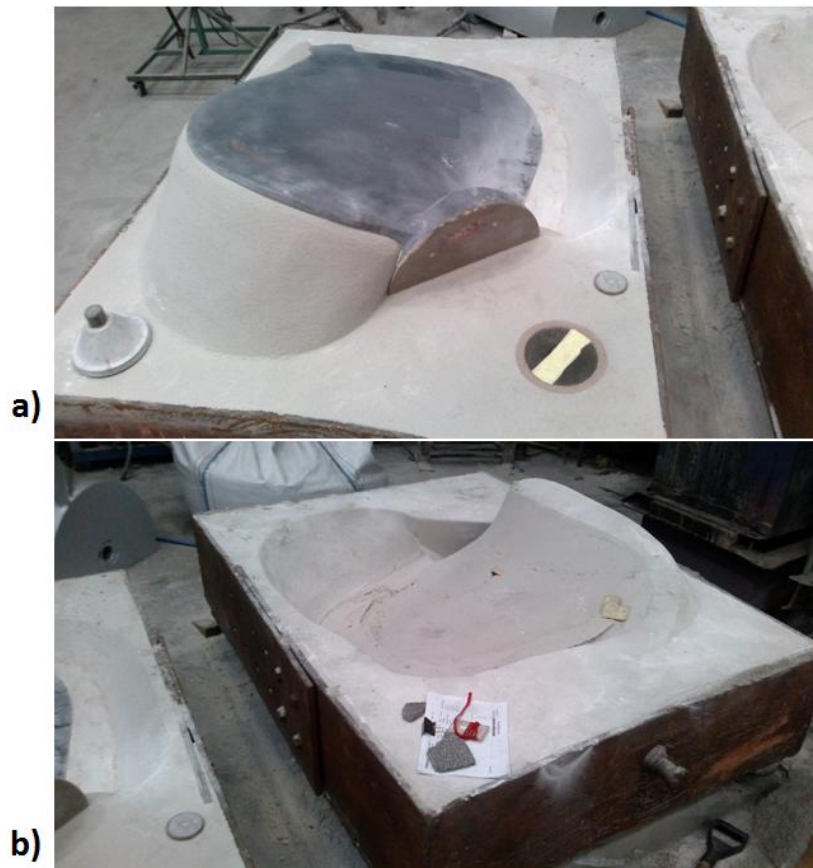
Moldação de uma pá de hélice de passo variável: a) moldação inferior; b) moldação superior.
